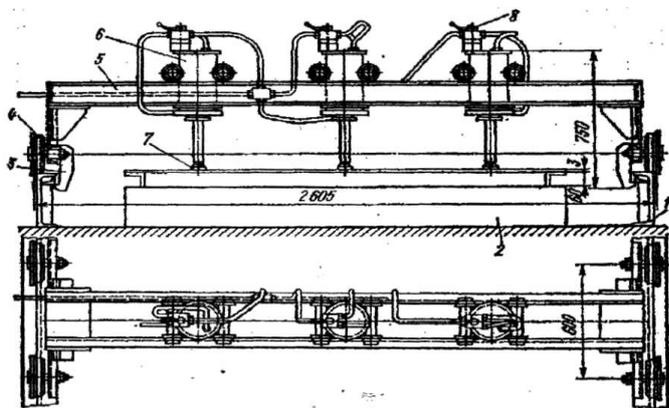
Стенд с передвижной балкой с пневмоцилиндрами
